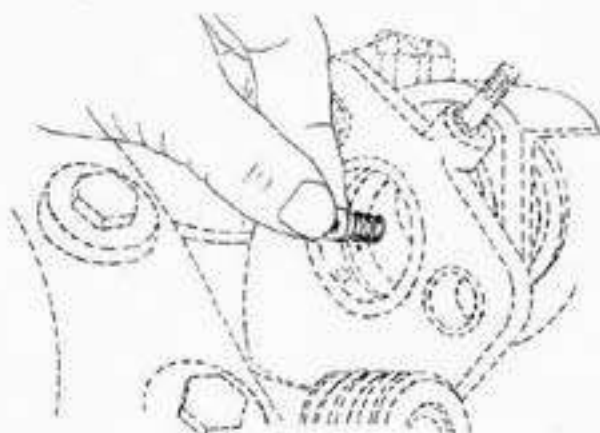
Die Dichtfläche mit der Druckfeder wird ausgebaut.
